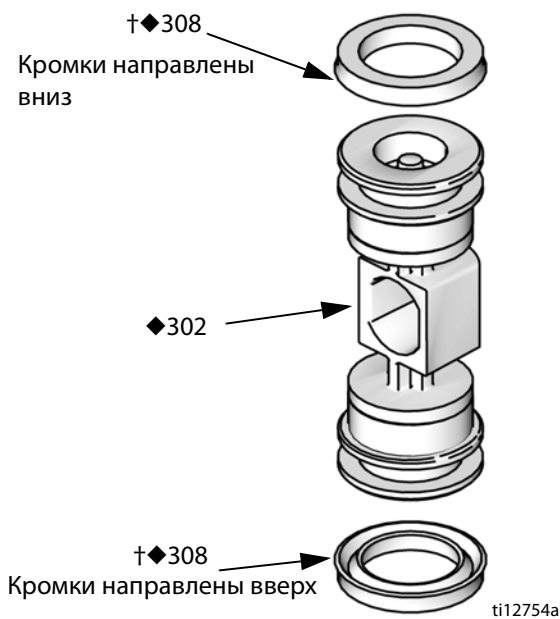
Установка П-образных уплотнений в воздушный клапан
